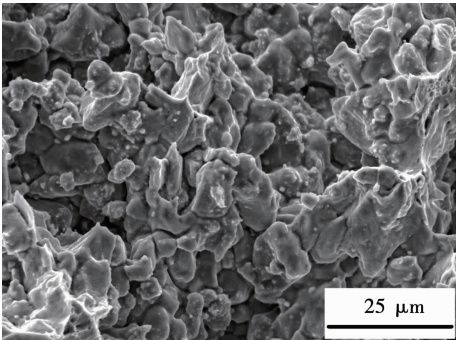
焊缝/T91 界面蠕变开裂断口形貌
